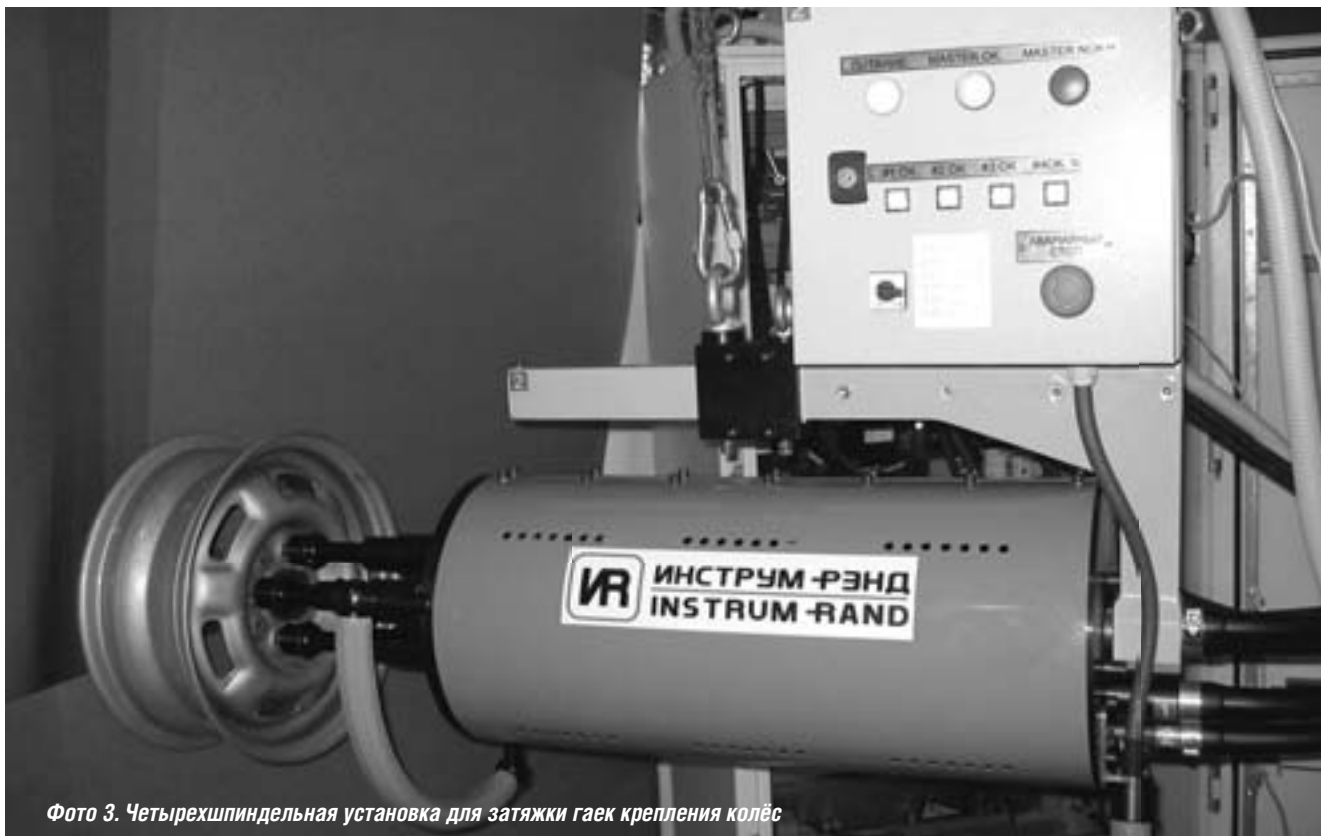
Четырехшпиндельная установка для затяжки гаек крепления колёс
